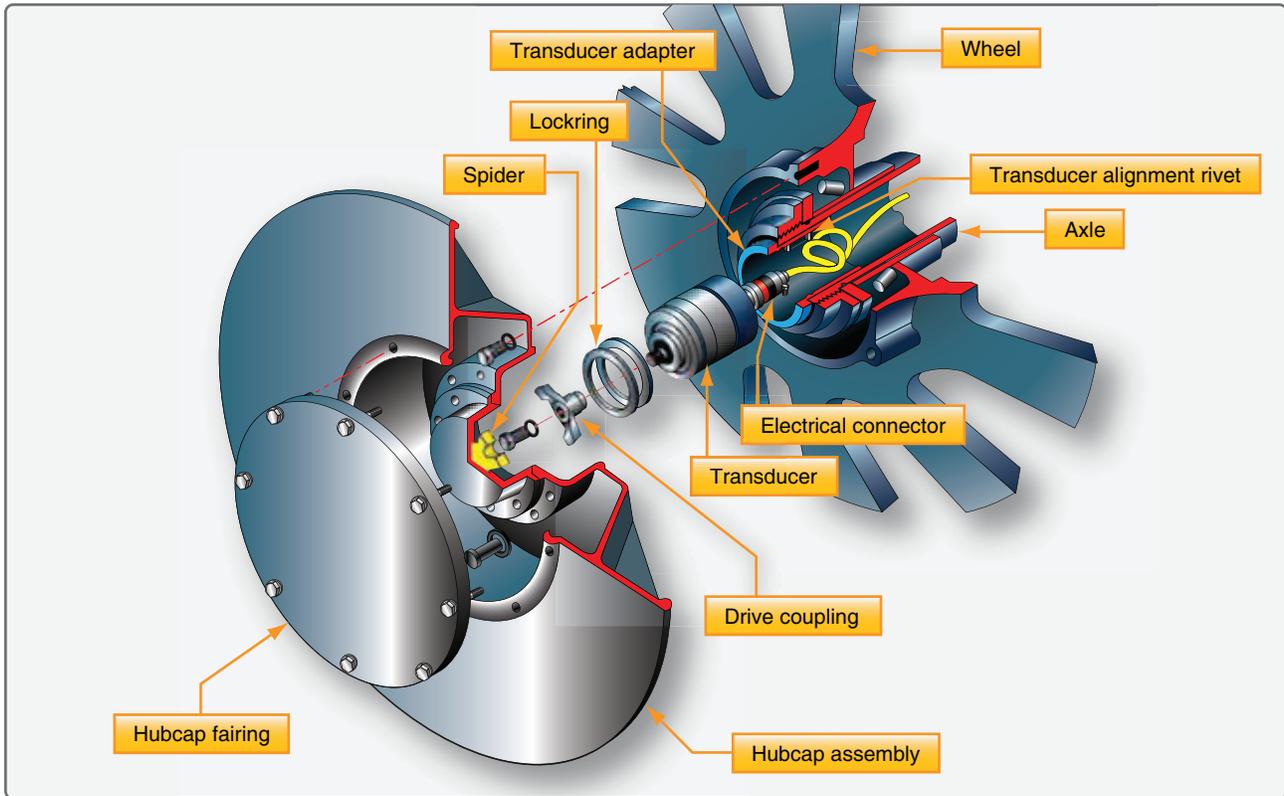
O estator de um sensor de rodas antiderrapagem está montada no eixo, e o rotor está acoplado ao cubo da roda de aranha que gira com a roda.
